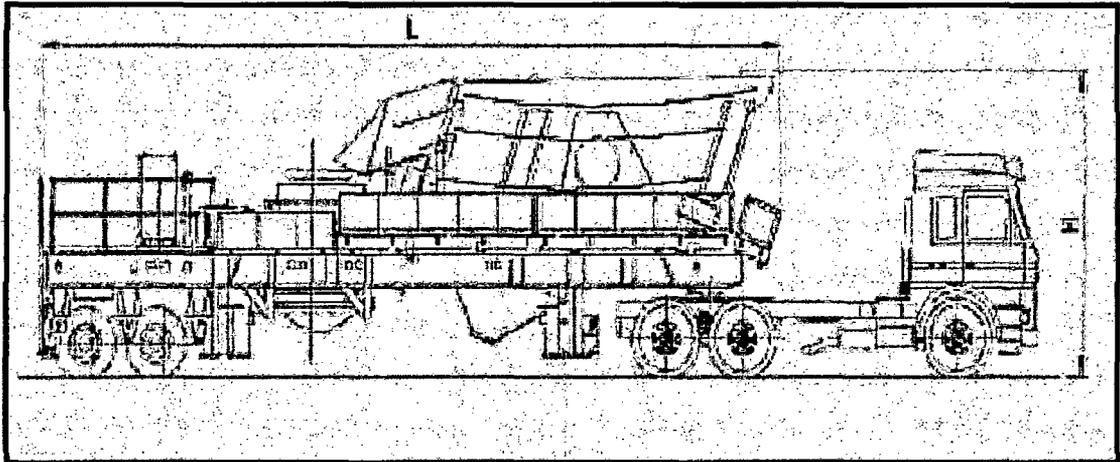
Vista del montaje para el transporte de la planta trituradora portátil según fabricante
